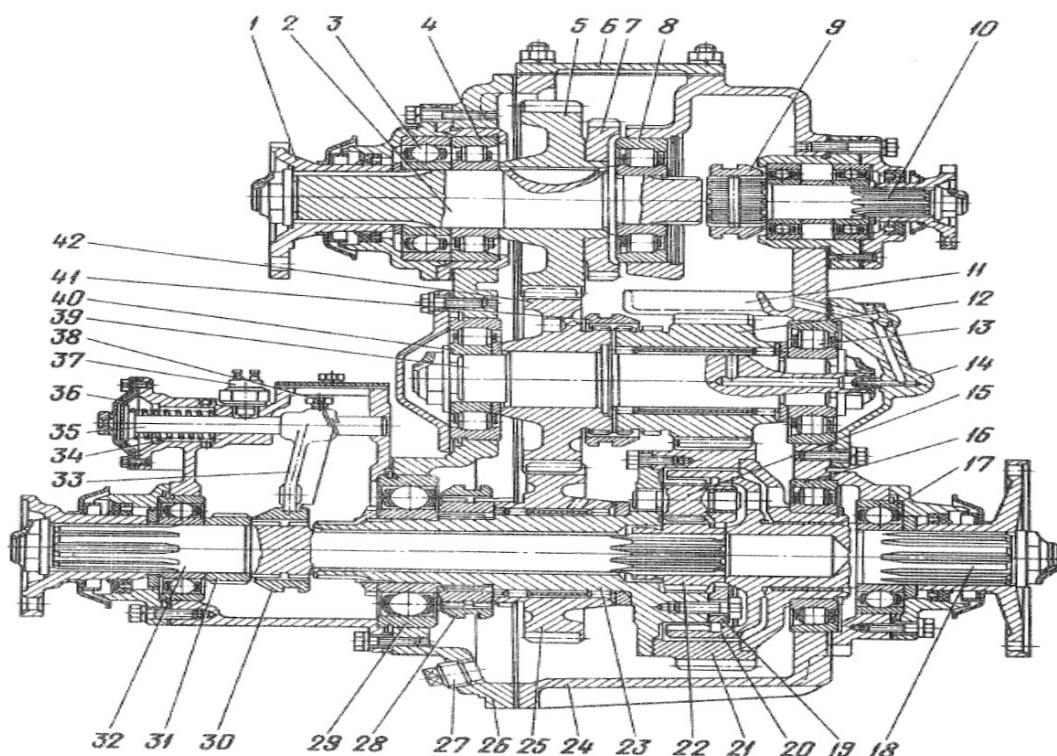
Раздаточная коробка автомобиля КамАЗ: Раздаточная коробка: 1 — фланец первичного вала; 2 — первичный вал; 3, 4, 8, 13, 16, 17, 29, 40 — подшипники; 5 — ведущее зубчатое колесо; 6 — крышка верхнего люка; 7 — зубчатое колесо отбора мощности; 9 — муфта включения коробки отбора мощности; 10 — коробка отбора мощности; 11 — маслосборник; 12 — зубчатое колесо низшей передачи; 14 — крышка подшипника; 15 — сателлит; 18 — вал привода задних мостов; 19 — задняя обойма дифференциала; 20 — коренное зубчатое колесо; 21 — зубчатое колесо низшей передачи дифференциала; 22 — солнечное зубчатое колесо; 23 — передняя обойма; 24 — картер раздаточной коробки; 25 — зубчатое колесо высшей передачи; 26 — крышка картера раздаточной коробки; 27 — магнитная пробка; 28, 30, 41 — муфты; 31 — ведущее зубчатое колесо привода преобразователя электрического спидометра; 32 — вал привода переднего моста; 33 — вилка; 34 — пружина; 35 — шток; 36 — мембрана; 37 — выключатель; 38 — стопорный болт; 39 — промежуточный вал; 42 — зубчатое колесо постоянного зацепления
